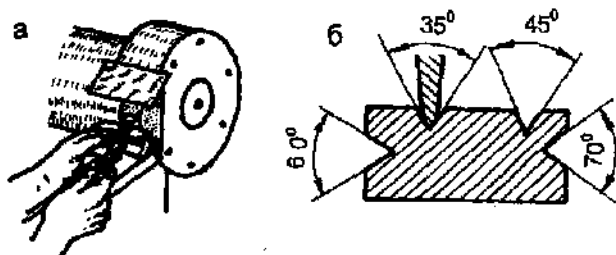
Заточка зубила (а) и шаблон для проверки угла заточки (б)
